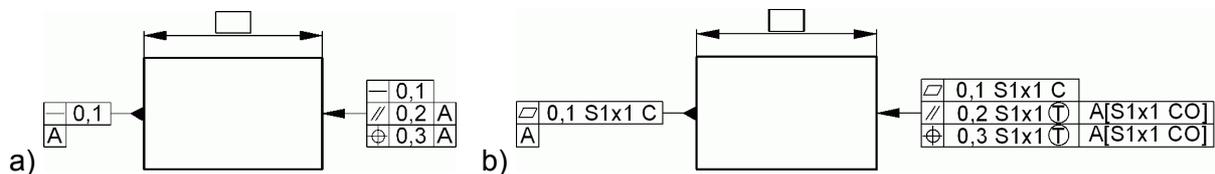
Toleranzen für Form, Richtung und Ort an zwei Oberflächen mit Bezug;
